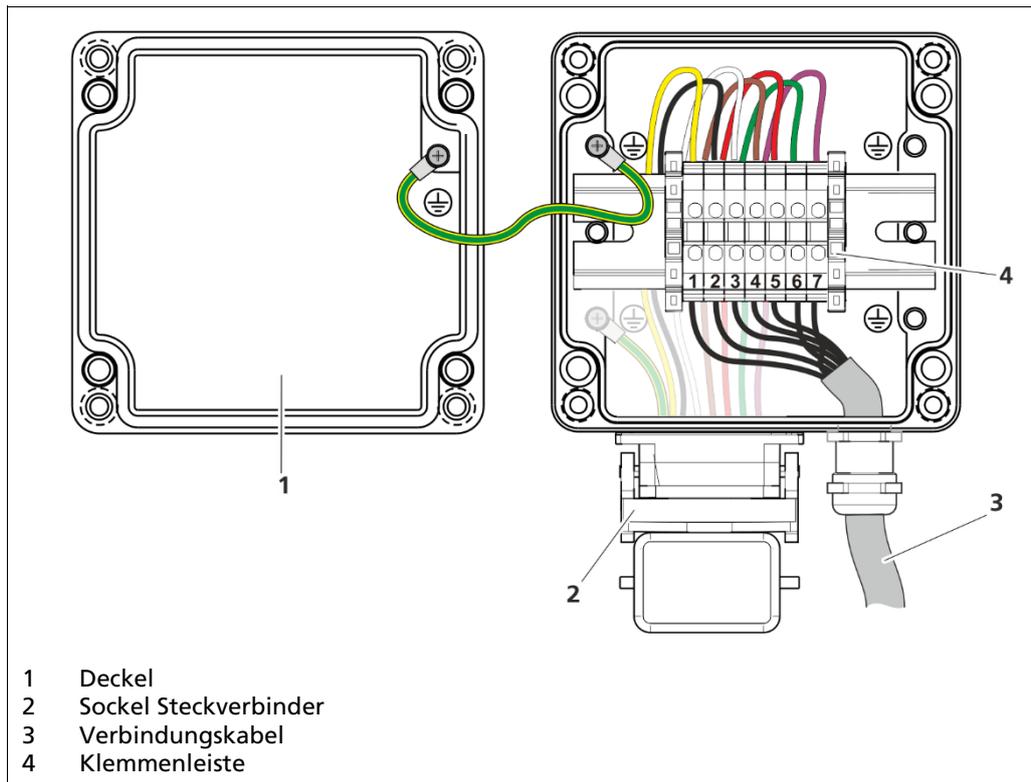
Anschlussbox anklemmen (Variante mit Industrie-Steckverbinder)
